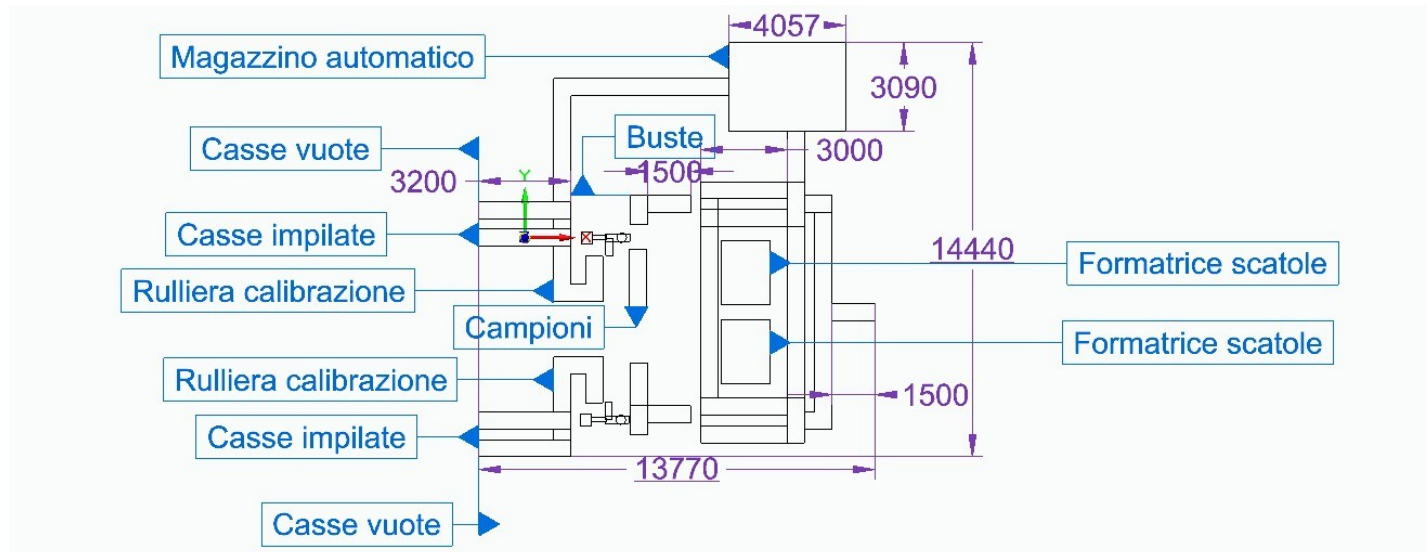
seconda soluzione per il layout del nuovo impianto di imballaggio. Dimensioni in millimetri
